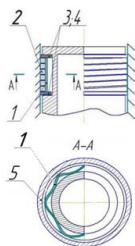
Принципиальная схема расположения поршня в цилиндре компрессора:
